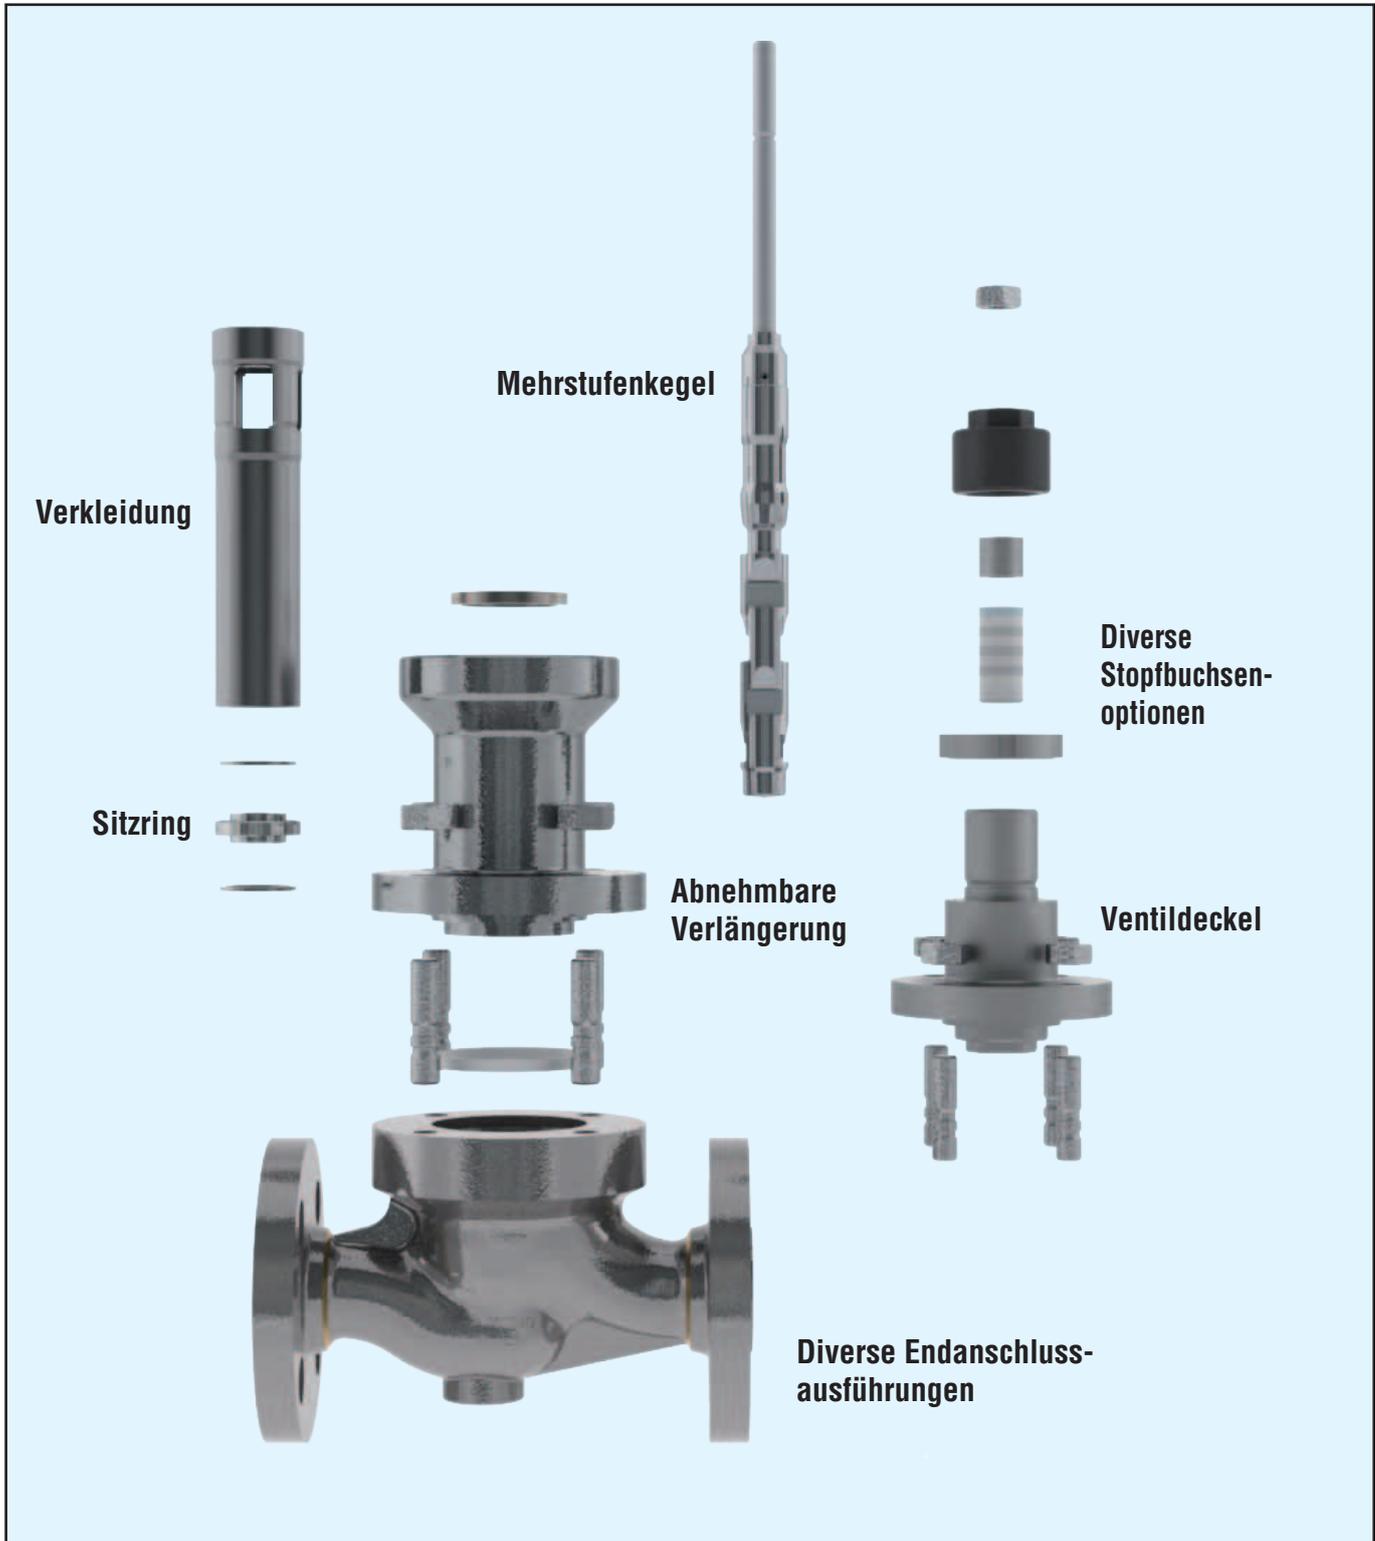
Explosionszeichnung (Durchgangsventil, Gussausführung)
